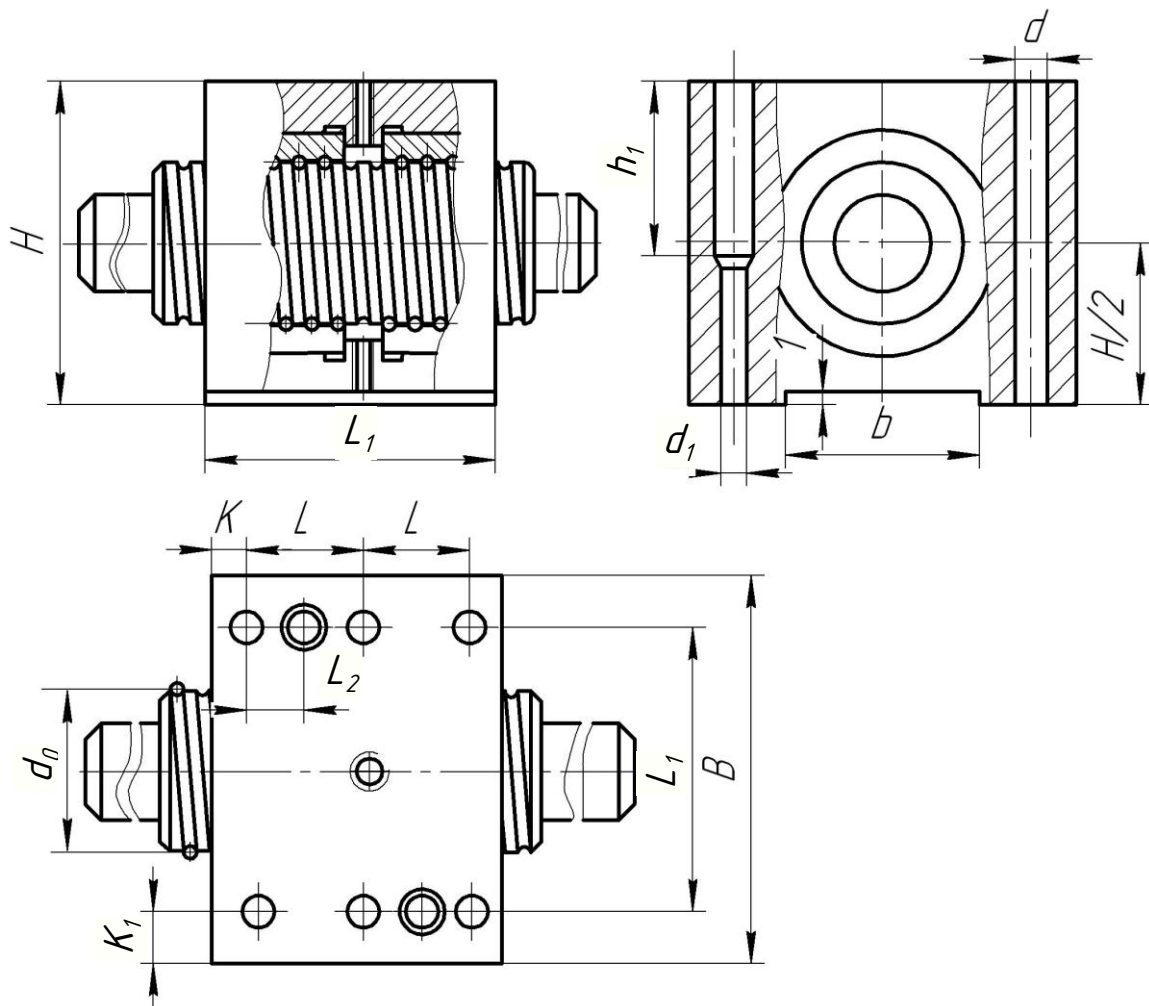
Конструкція кулькової гвинтової передачі у прямокутному корпусі
